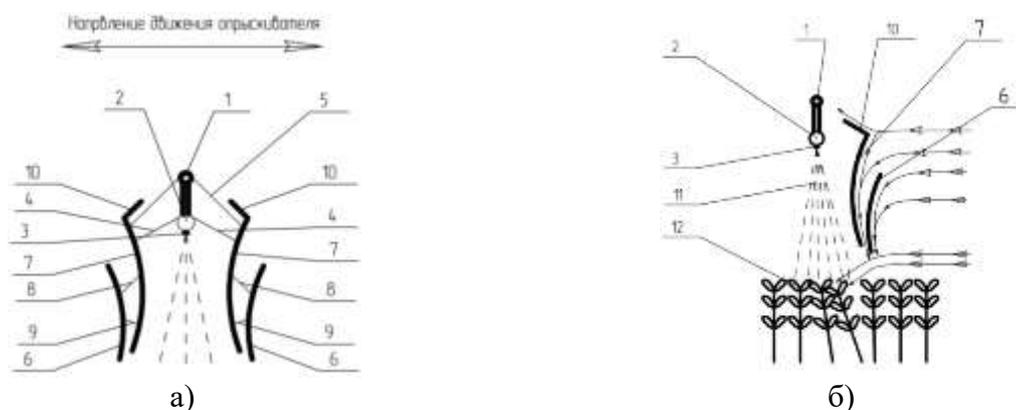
Ветрозащитное устройство комбинированного действия с использованием щитков: 1 – несущая конструкция; 2 – распределительная штанга; 3 – распылитель; 4, 5, 8, 9 – кронштейны; 6 – наружный щиток; 7 – внутренний щиток; 10 – козырек; 11 – факел распыла; 12 – посевы сельскохозяйственной культуры
